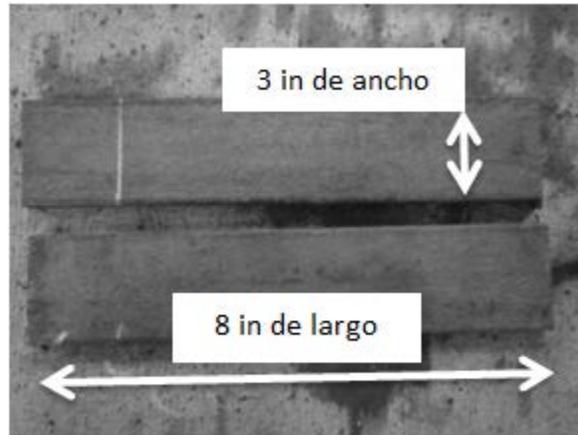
DIMENSIONES DE LA PROBETA DE SOLDADURA
